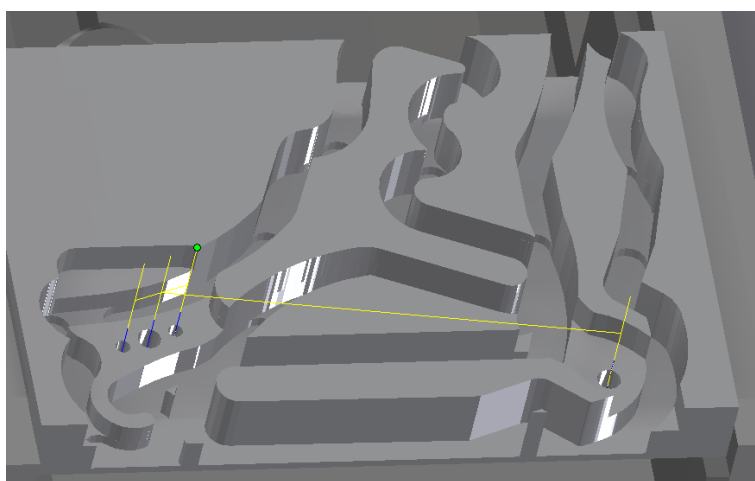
Dráha – frézování otevřených kapes. [Autodesk Inventor HSM 2019]
